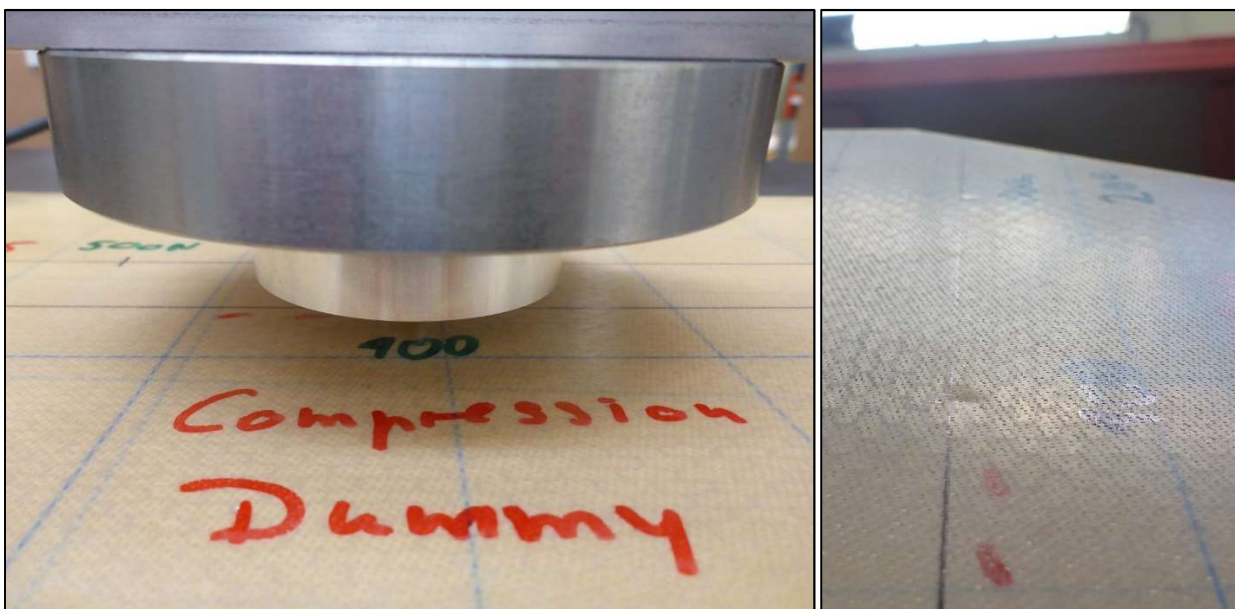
Test #5: Druckkraft F [N]: 400, inkl. Abdruck
